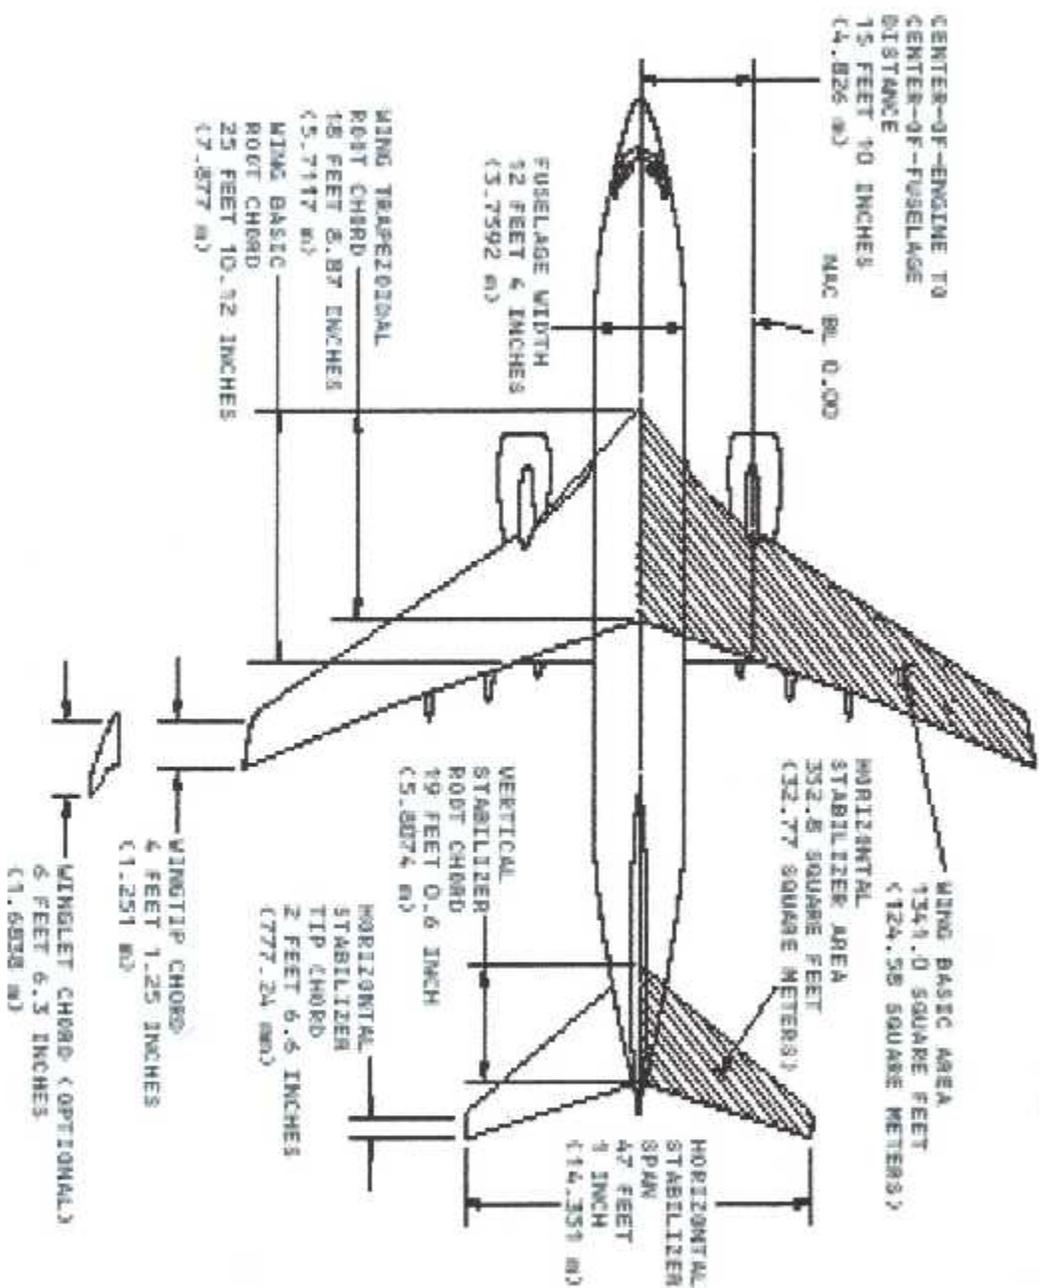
LES PRINCIPALES DIMONSION ET SURFACES (VUE DESSUS)
